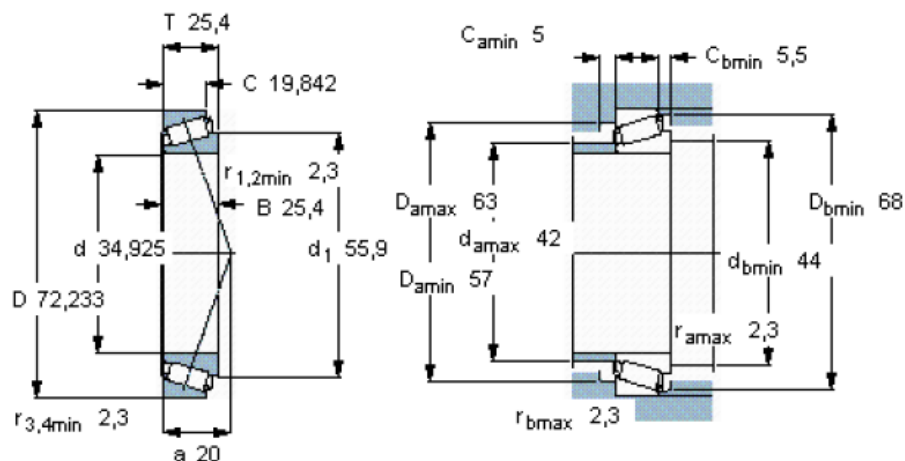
Dimensiones del cojinete HM 88649/2/610/2/QCL7C [14].
